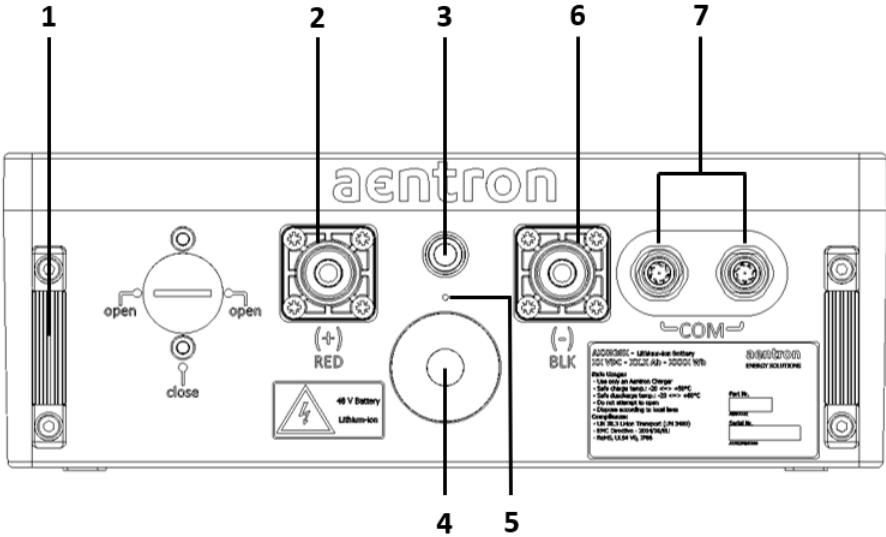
Anschlüsse, Elemente (2 kWh Typ R+M)
